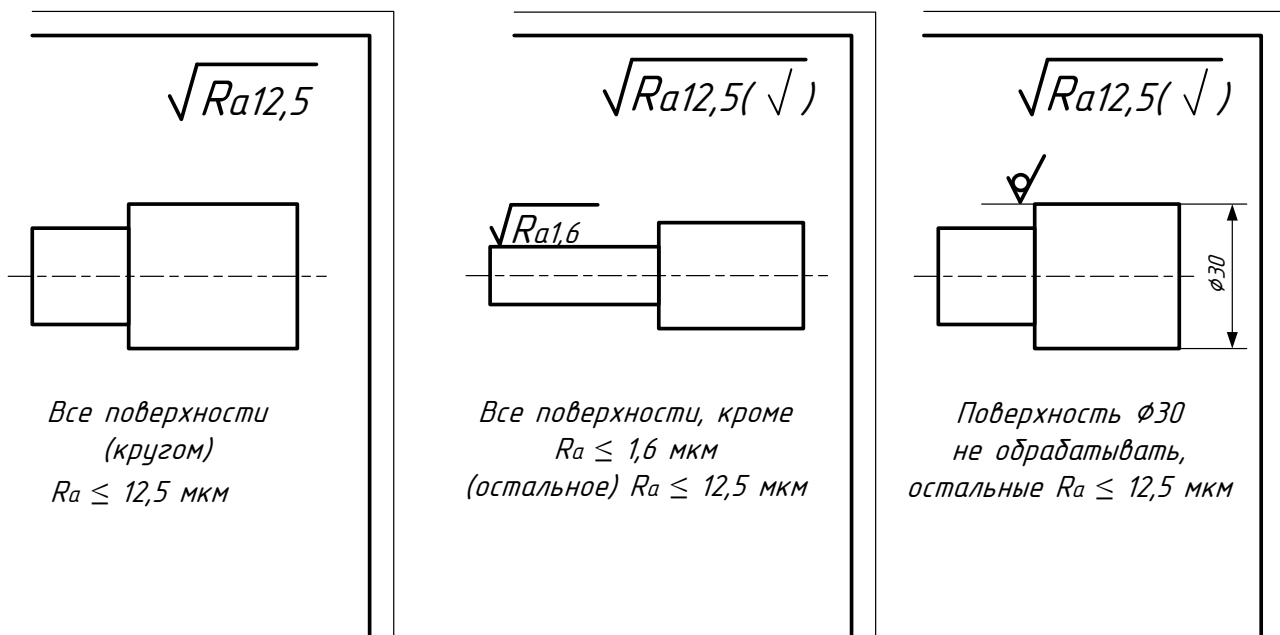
Варианты обозначения шероховатости для части поверхностей изделия на чертеже
